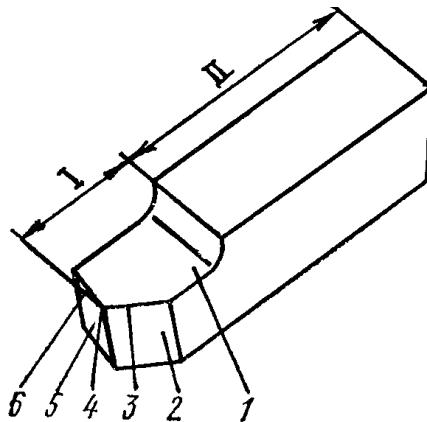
Конструкция и элементы токарного прямого проходного резца:
